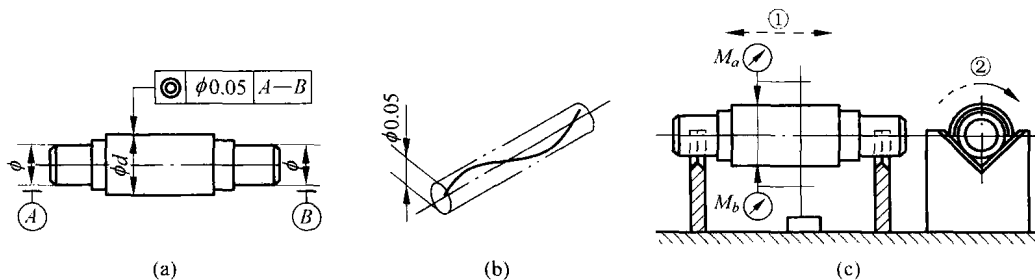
同轴度公差标注、公差带及检测方法
